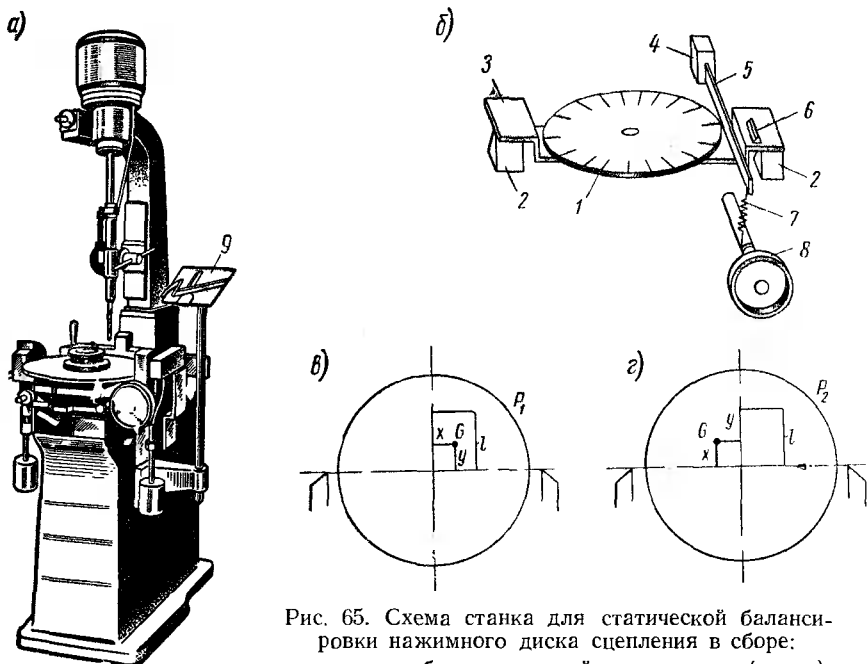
Схема станка для статической балансировки нажимного диска сцепления в сборе:
